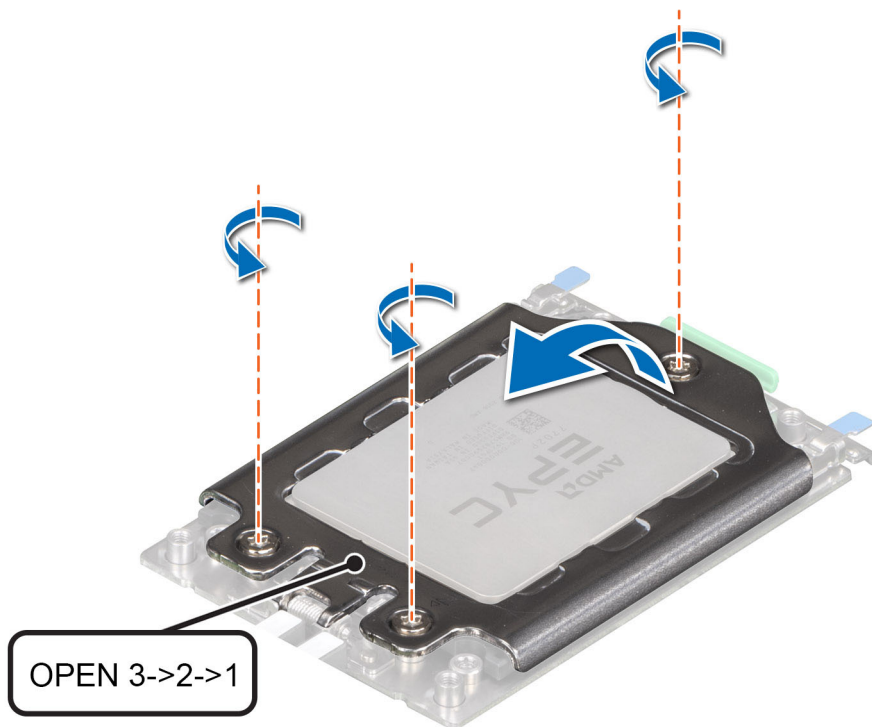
Entfernen der Schrauben auf der Kraftplatte
